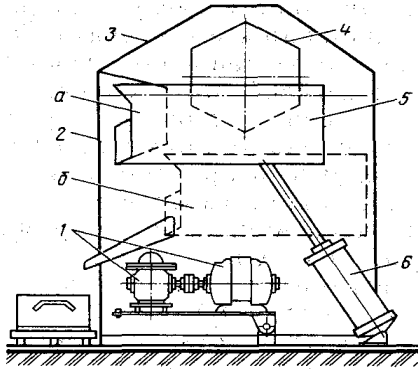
5. Установка для миття дрібних деталей в обертовому барабані:
